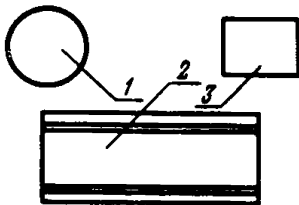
Типовая схема планировки рабочего места разборки передней оси:
